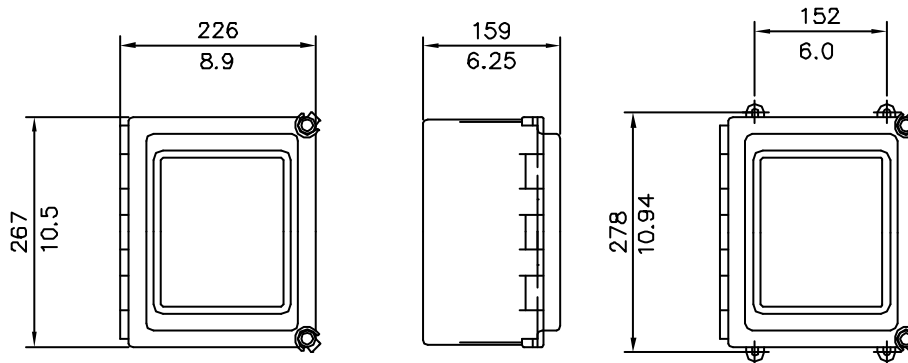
Transmisor indicador: dimensiones (mm/in) y medida de los pies para montaje
